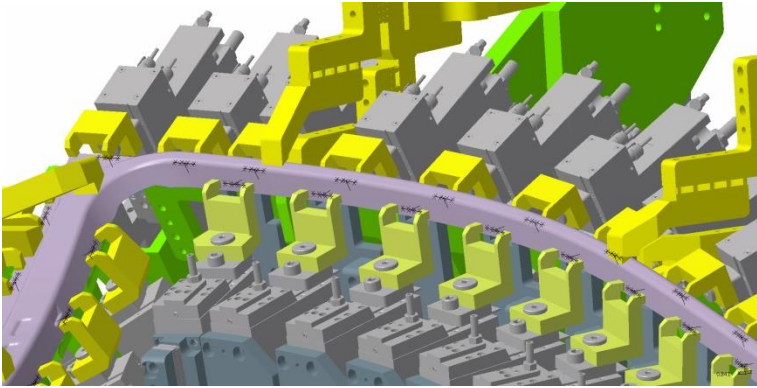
Spanntechnik des Robscan-Laserschweißens am Beispiel eines Fensterrahmens
